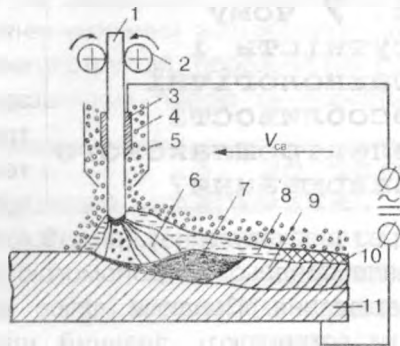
Схема автоматичного зварювання під флюсом: 1 - електрод, 2 - механізм подачі дроту, 3 - провідник струму, 4 - флюс, 5 - бункер, 6 - зварювальна дуга, 7 - зварювальна ванна, 8 - шлакова ванна, 9 - зварювальний шов, 10 - шлакова кірка, 11 - основний метал.
